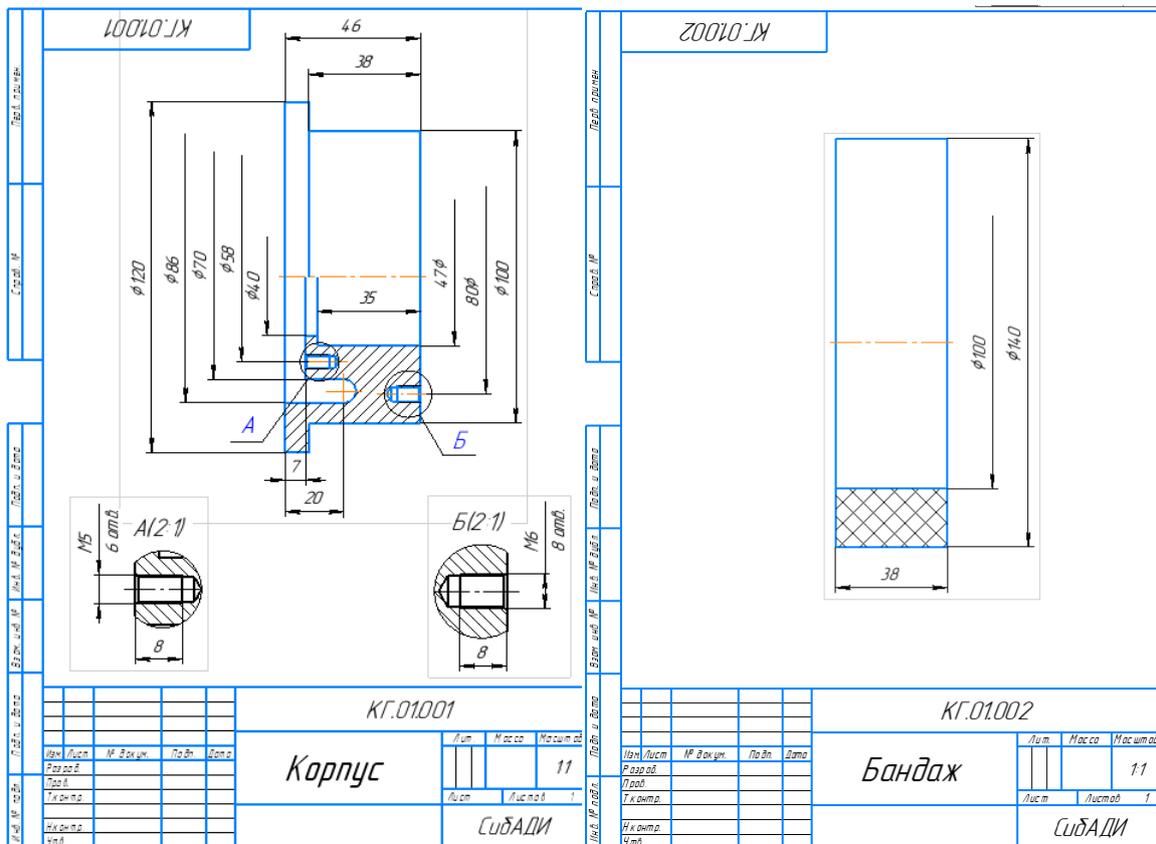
Чертежи деталей «Корпус» и «Бандаж»
